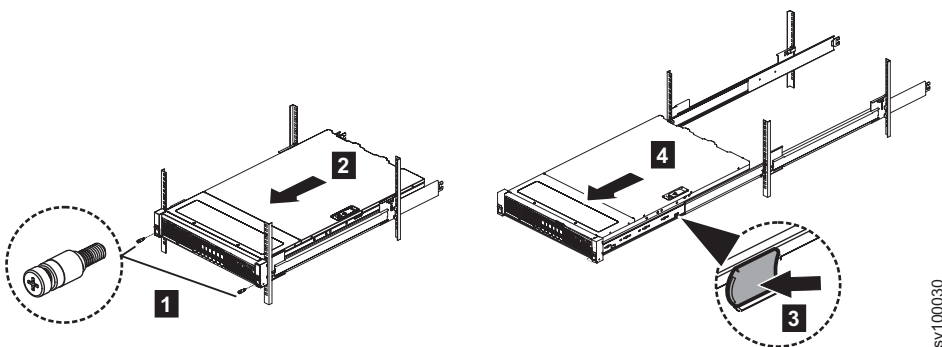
Remova o chassi do nó 2145-SV1 do rack
